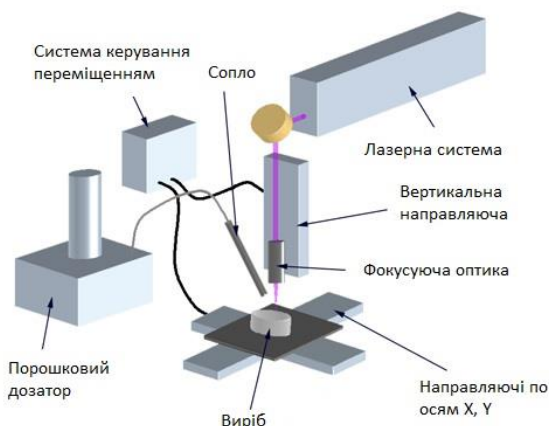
Схема обладнання для газопорошкового лазерного наплавлення[3]
